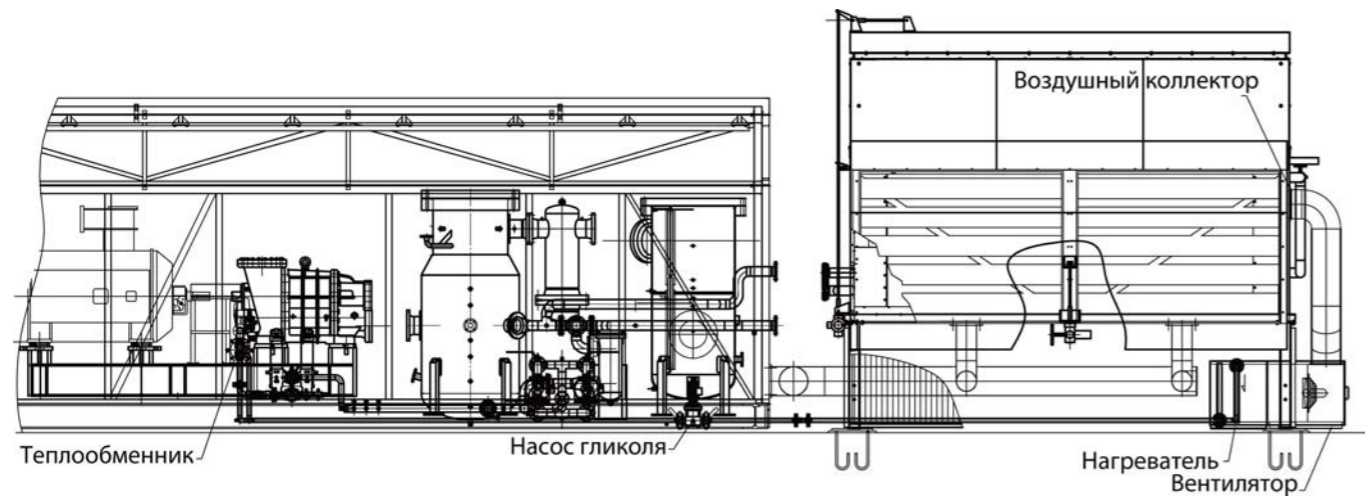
Компоновка компрессорной установки (фронтальный вид)
